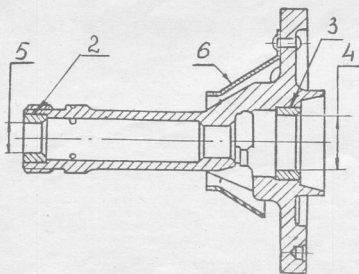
Ротор центробежного фильтра в сборе со втулками и отражателем.
